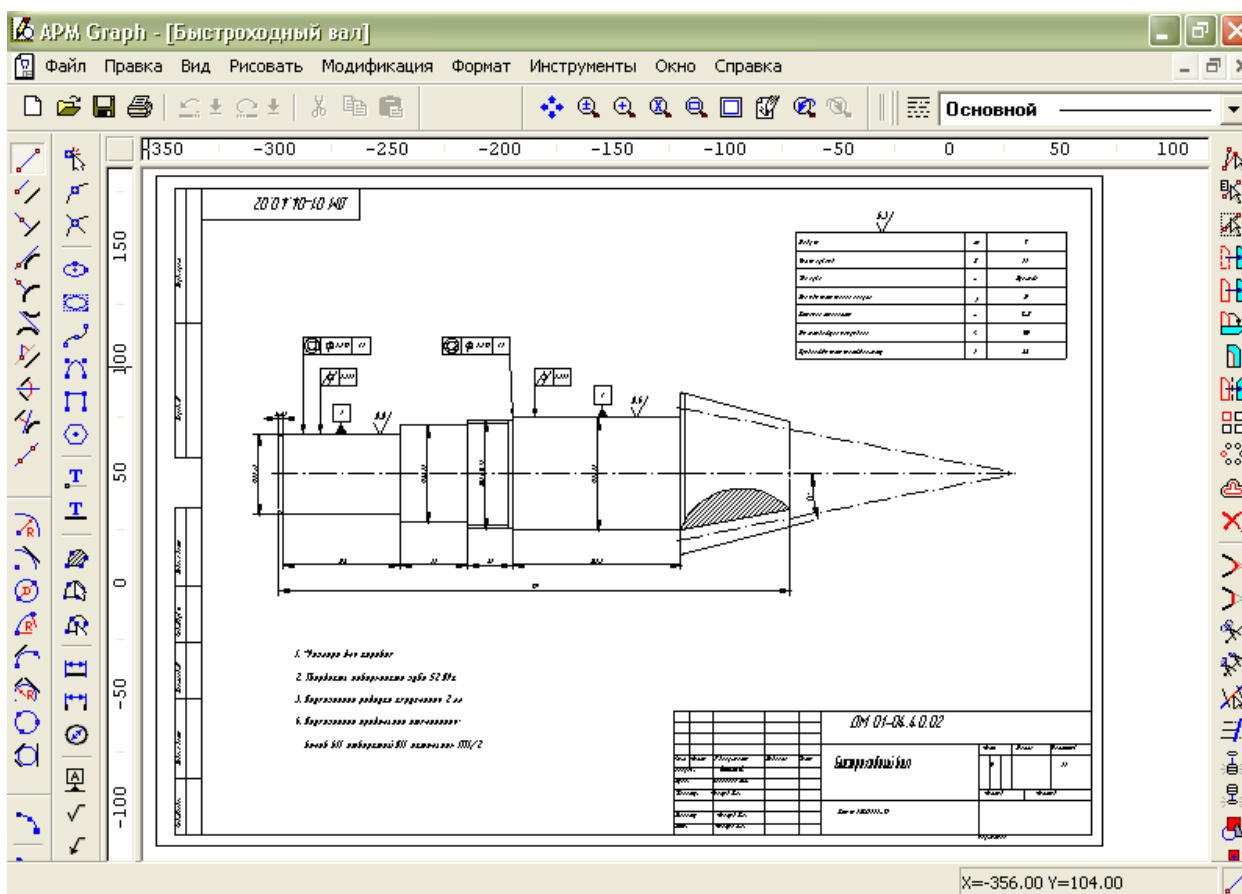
Рабочий чертёж вала – шестерни быстроходной ступени редуктора
